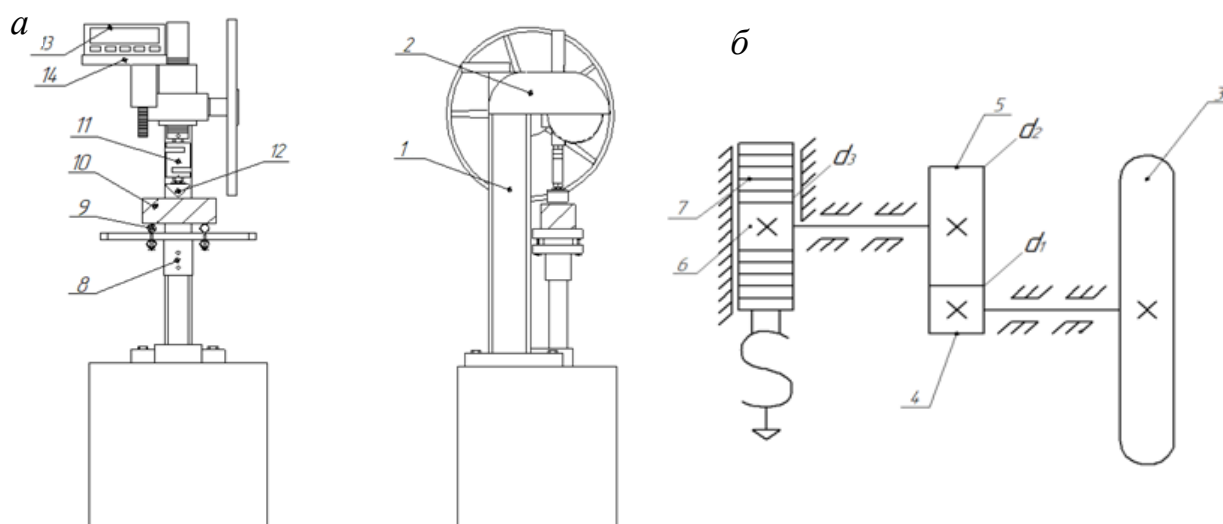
Устройство (а) и кинематическая схема (б) стенда для реализации разрушающей нагрузки и контроля изгибной прочности формованной торфяной продукции
